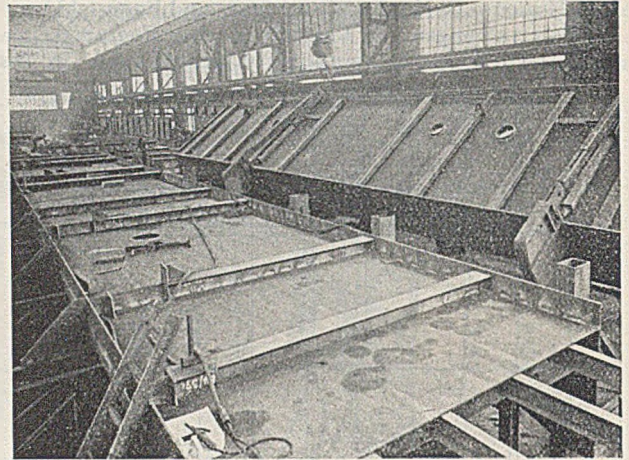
Arbeitsplatz 2. Stegbleche und Gurtplatten werden in einer Vorrichtung zusammengebaut, die äußeren Aussteifungen angeheftet und die obere Seite fertig geschweißt. Dann werden die Träger in einer Kippvorrichtung um 90° gedreht und die unteren Querträgerstücke und Längsaussteifungen des unteren Gurtes aufgeschweißt.
